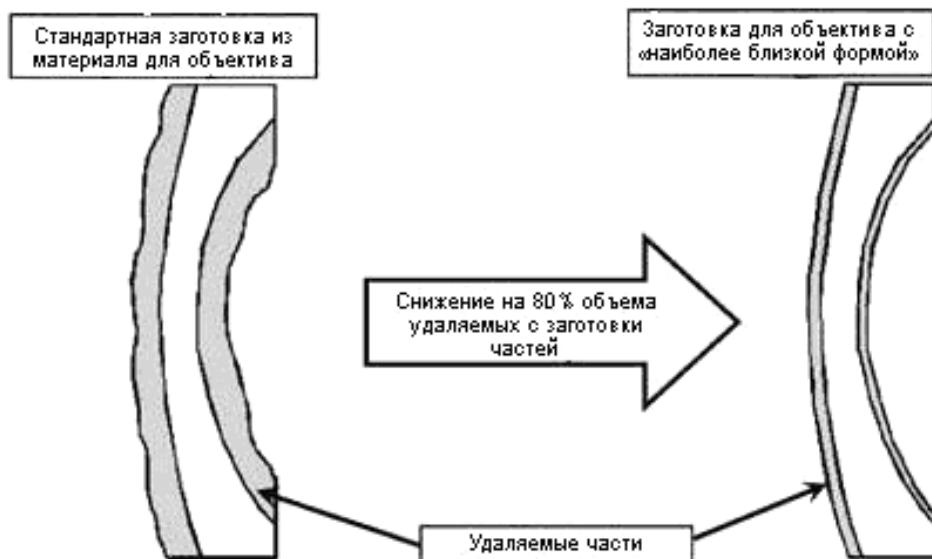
Заготовка с «наиболее близкой формой» для объектива
